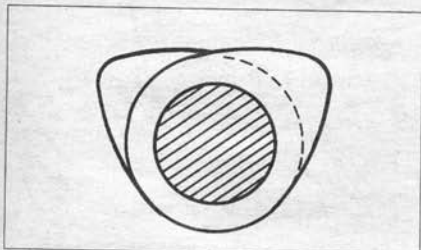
Положение кулачков первого цилиндра при укладке распределительного вала в опоры головки цилиндров
